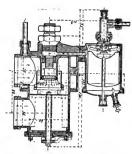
Longuemare-Karburator B 18 för 1³/_a pferdige Motore.
